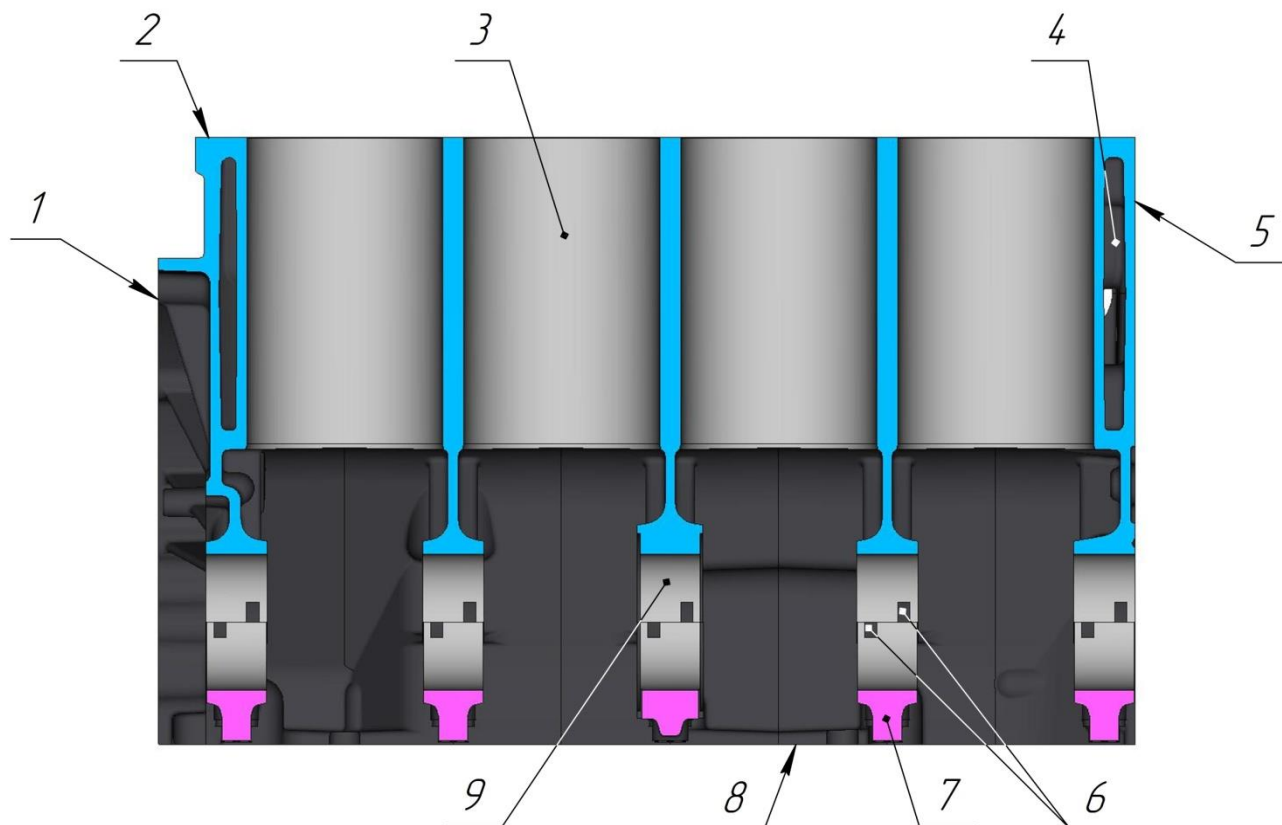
Блок цилиндров. Продольный разрез по оси цилиндров:
